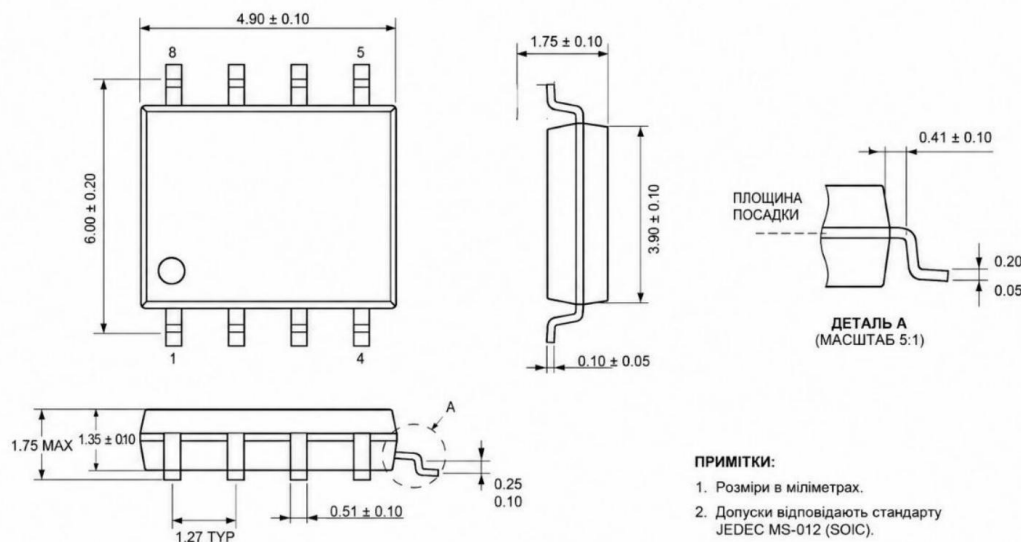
Зовнішній вигляд і розміри корпусу лінійного стабілізатора напруги ADP150AUJZ-3.3-R7
